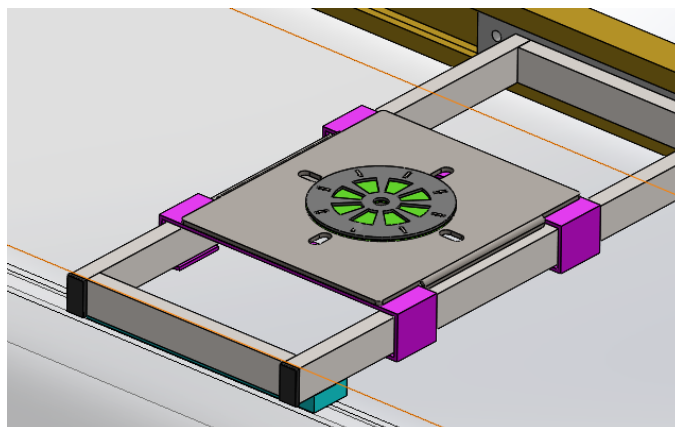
Подшипник с роликами от игольчатого подшипника
